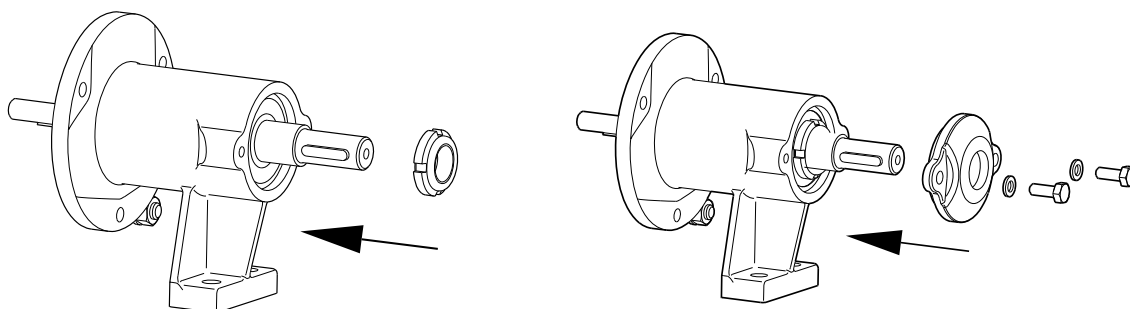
Монтаж корончатой гайки и крышки подшипника
